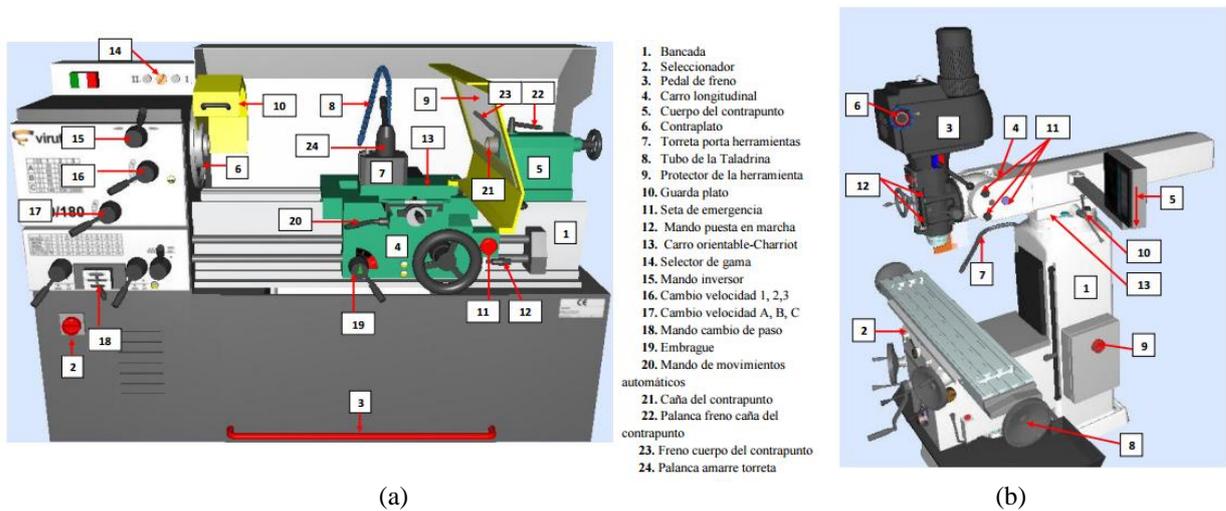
Identificación de las partes principales de la máquina herramienta: (a) torno y (b) fresadora.
